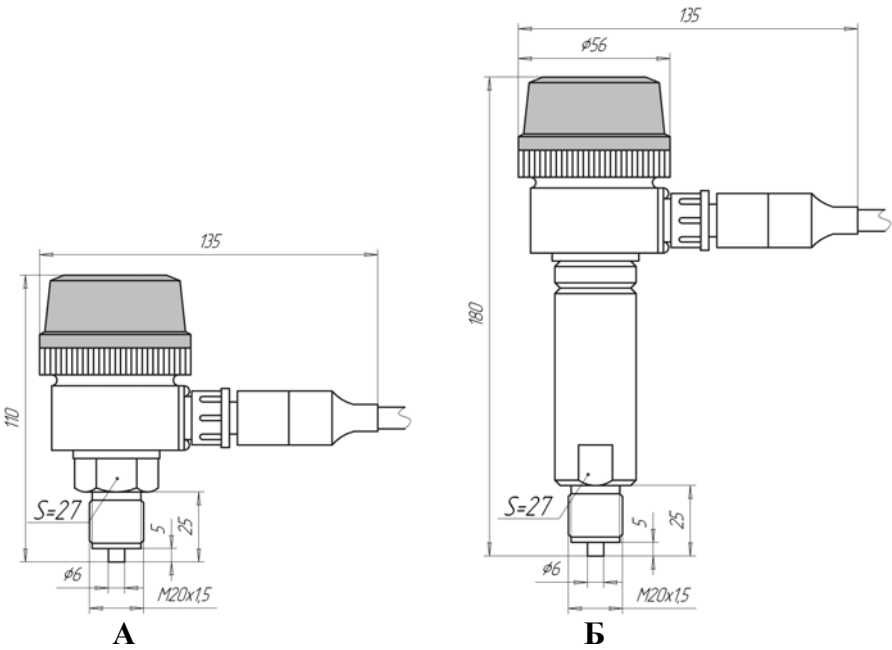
Модель 1120. Нержавеющий корпус, герморазъем.
